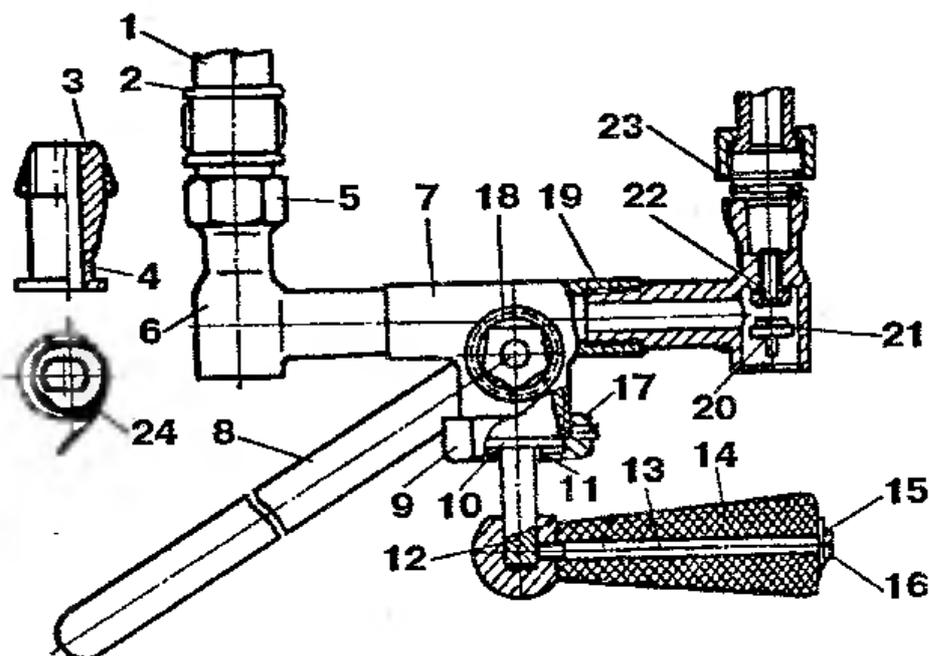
Смеситель с пробковым переключателем «ванна-душ»: 1 — подводящая труба; 2 — муфта; 3 — уплотнение втулки; 4 — эксцентрическая втулка; 5 — накидная гайка; 6 — боковина; 7 — корпус; 8 — излив; 9 — накидная гайка; 10 — шайба латунная; 11 — ограничитель; 12 — остов; 13 — ось; 14 — рукоятка; 15 — шайба; 16 — специальный винт; 17 — стопорный винт; 18 — конус (пробка); 19 — уплотнение; 20 — клапан; 21 — прокладка головки крана; 22 — втулка ремонтная; 23 — прокладка накидной гайки; 24 — направление намотки уплотнения
